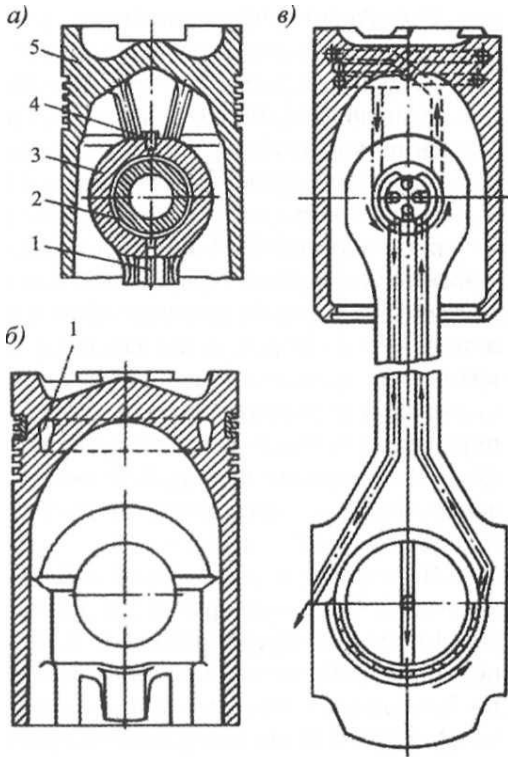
Способы охлаждения поршней тронковых двигателей
